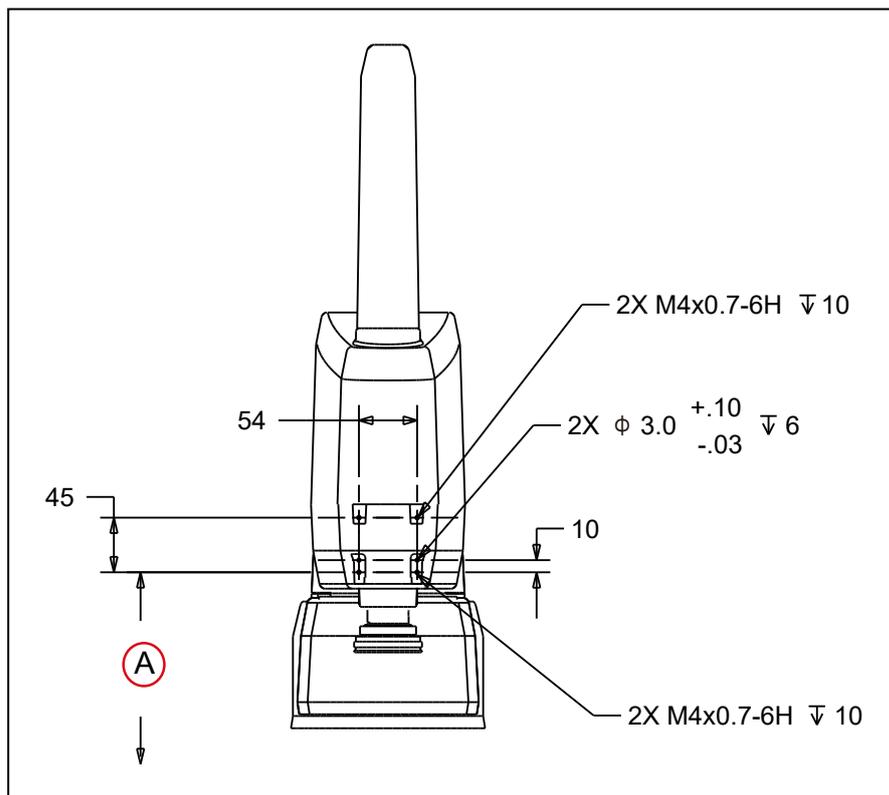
(A) eCobra 600 和 800 的摄像头支架安装尺寸 (单位: mm) (至底座 457 mm)
